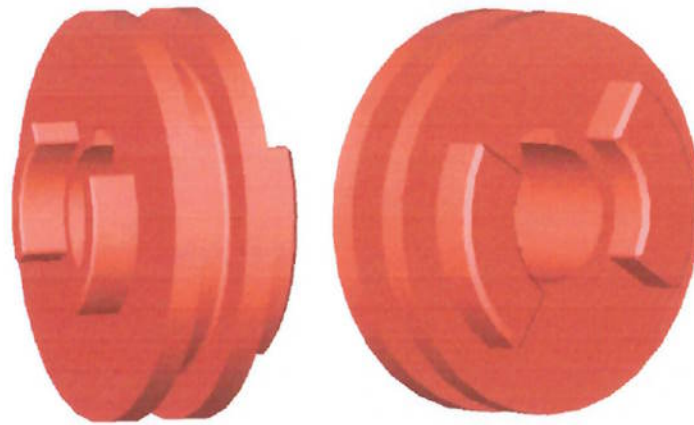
Duas vistas isométricas da embreagem de dentes
